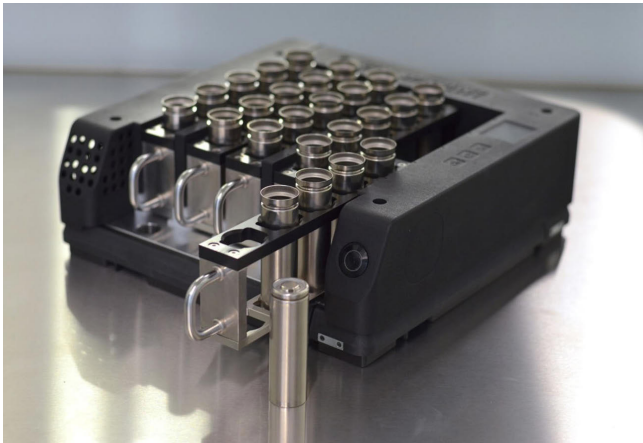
Intelligenter Werkstückträger. Foto: Fraunhofer IPA
